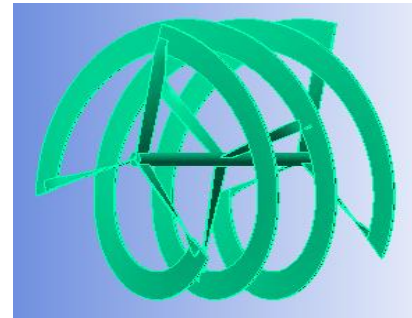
Общий вид трехзаходной фрезы РСО
